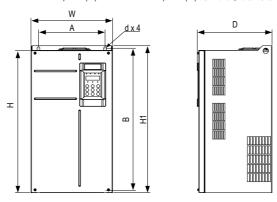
MD290T45G/55P(B)~MD290T160G/200P 外型尺寸及安装尺寸示意图
